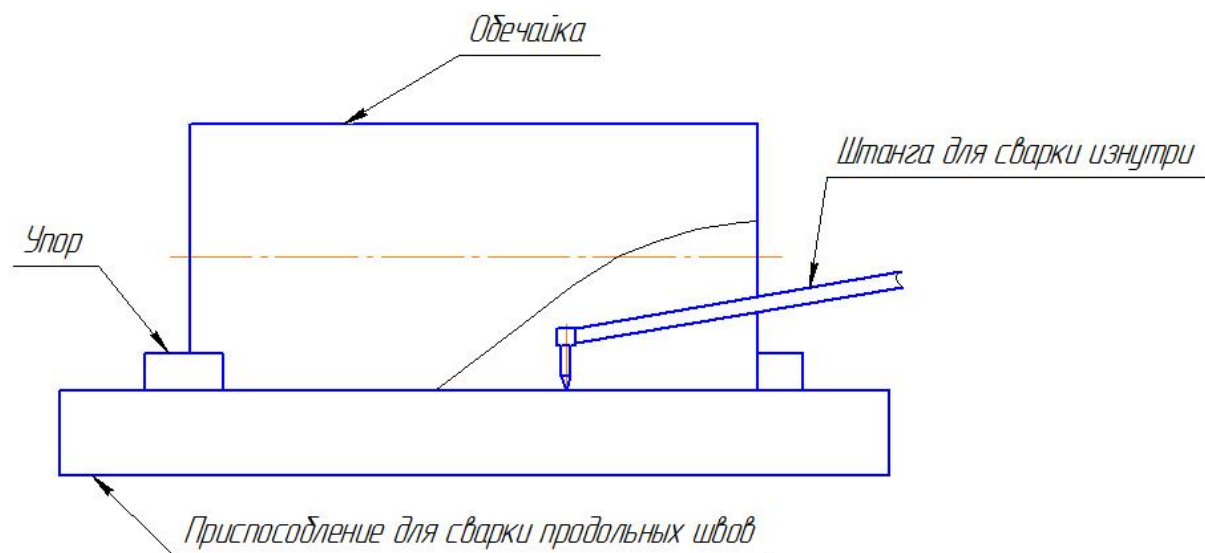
Позиция обечайки в приспособлении для сварки изнутри
